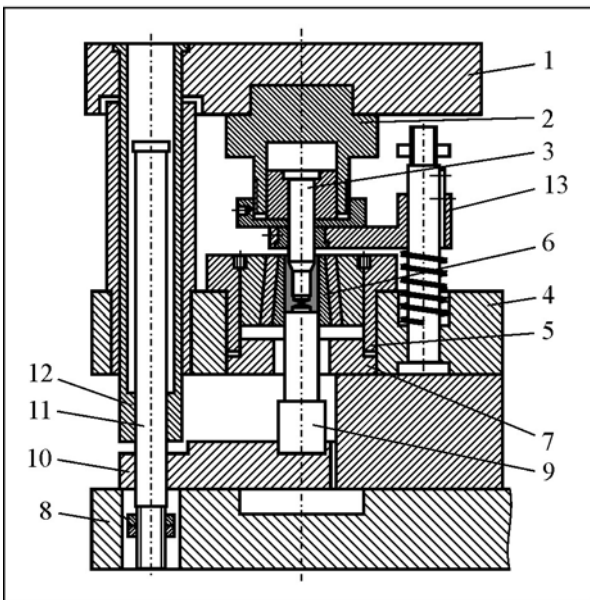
Схема штампа для видавлювання з матрицею, що плаває
